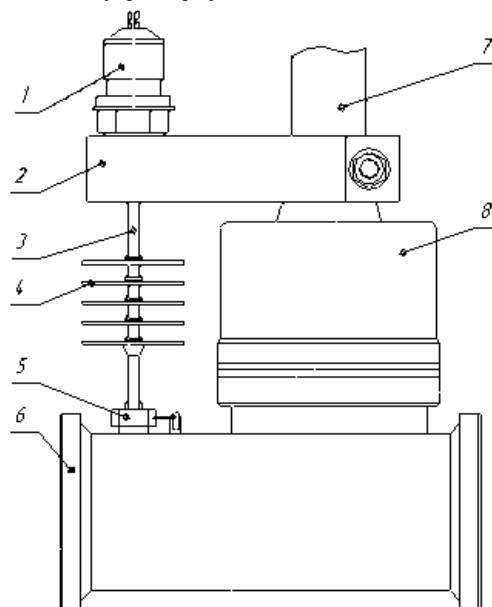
Конструктивная схема: 1 – датчик давления; 2 – кронштейн; 3 – капиллярная трубка; 4 – диск; 5 – штуцер; 6 – проточная часть; 7 – стояк; 8 – корпус
